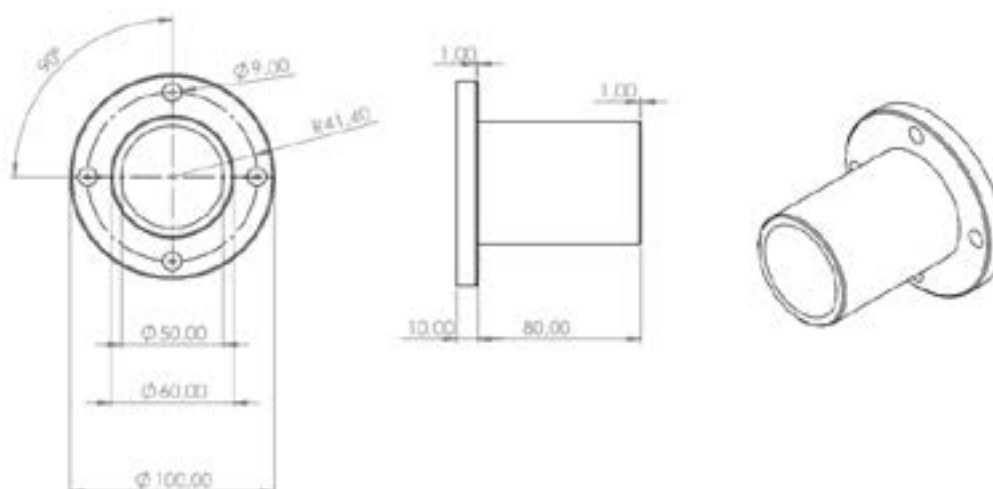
Desenho técnico flange comercial. Do autor (2021)
